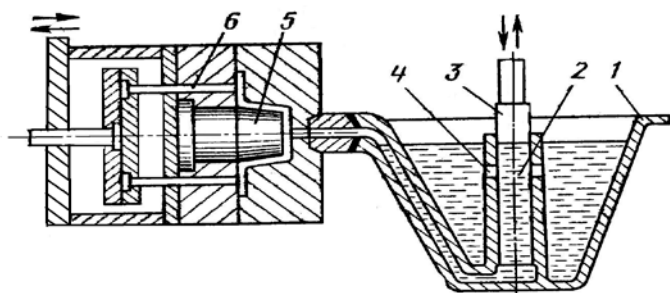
Схема процесса изготовления отливок на машинах с горячей камерой прессования: 1 – тигель; 2 – камера прессования; 3 – плунжер; 4 – отверстие; 5 – полость пресс-формы; 6 – выталкиватель
